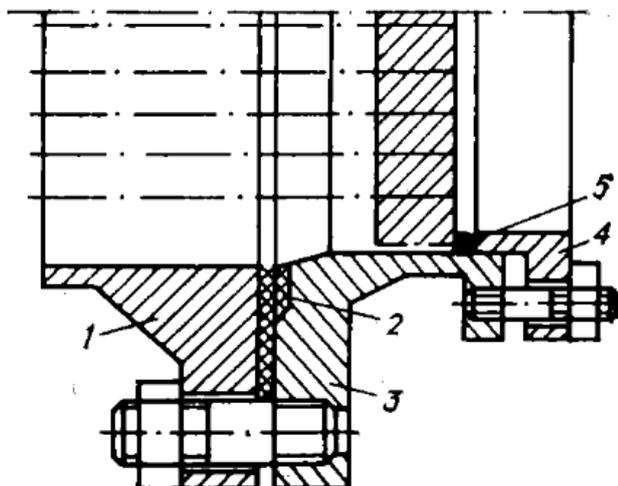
Приспособление для опрессовки: 1 – корпус; 2 – резиновая прокладка; 3 – фланец; 4 – прижимная втулка; 5 – резиновый шнур.
